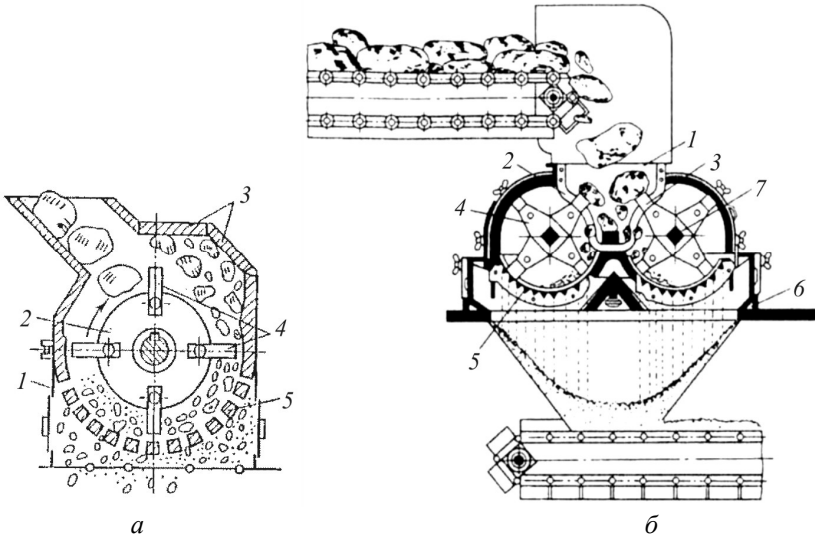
Молотковая однороторная (а) и двухроторная (б) дробилка с параллельным расположением роторов: 1 – загрузочная воронка; 2 – фигурные колосники; 3 – молотки; 4 – держатели молотков; 5 – колосниковые решетки; 6 – корпус дробилки; 7 – роторные валы
